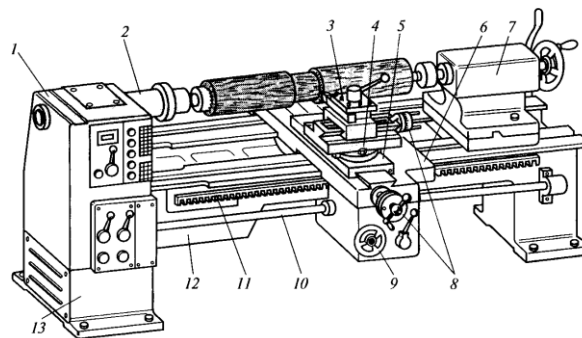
Токарний верстат з механічною подачею супорта і приставним лобовим пристроєм: 1 – передня бабка; 2 – шпиндель; 3 – різцетримач; 4 – додатковий поздовжній супорт; 5 – поперечний супорт; 6 – поздовжній супорт; 7 – задня бабка; 8, 9 – маховички; 10 – ходовий вал; 11 – рейка; 12 – станина; 13 – тумба
